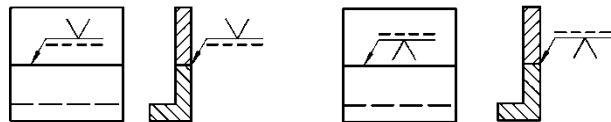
Ejemplo 1, Soldadura a tope
